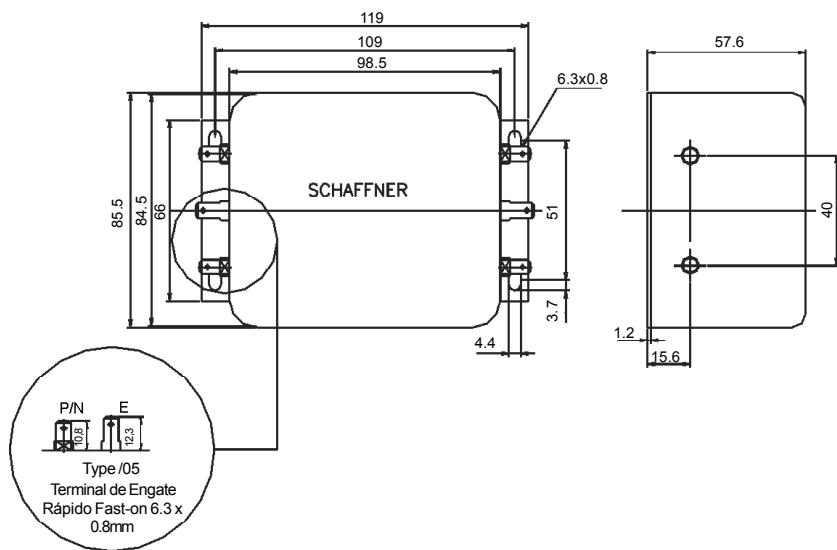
Desenho do filtro externo FS6007-16-06
